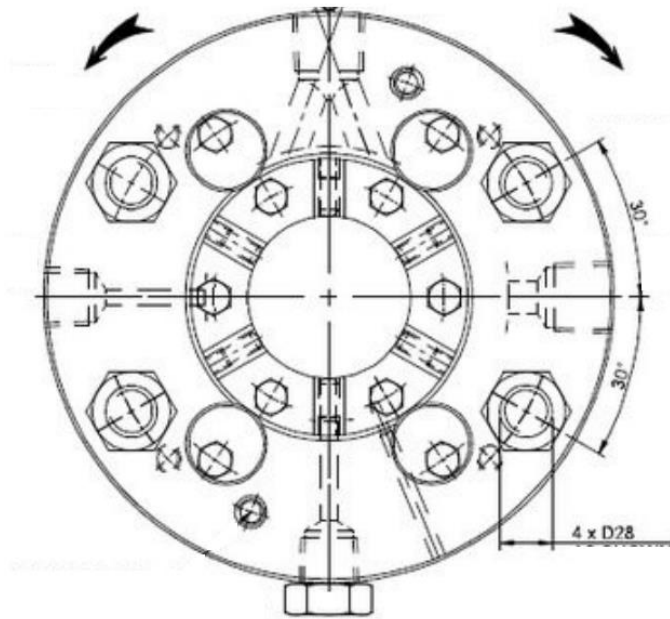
Геометрические размеры уплотнителя 369HRP/369
